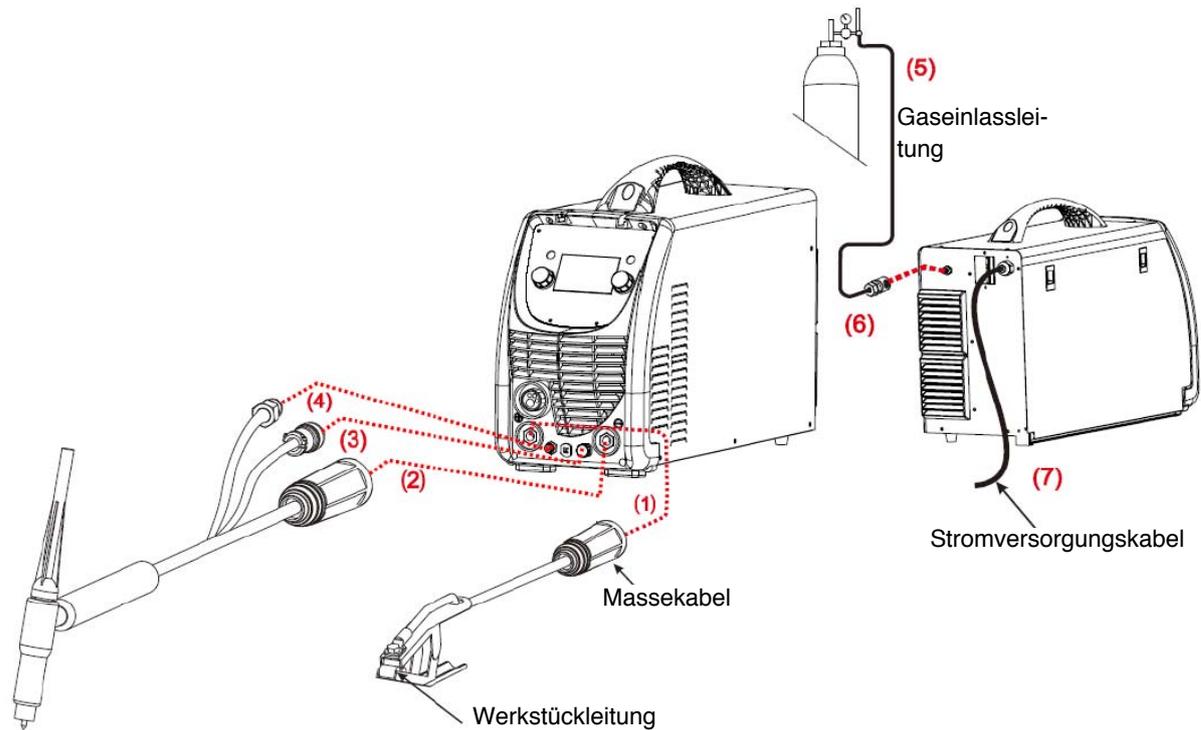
Einrichten des TIG-Schweißverfahrens beim Craft-Mig 253 LCD Synergic
